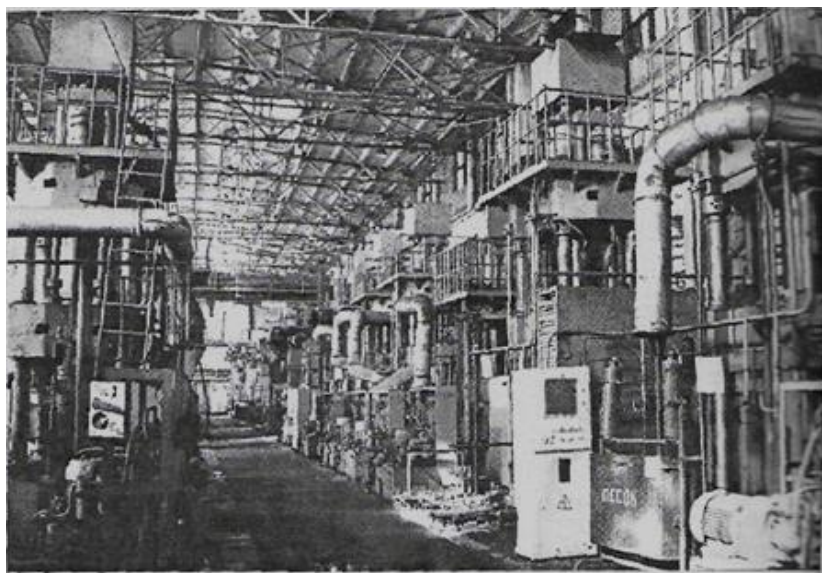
Участок гидравлических прессов для изотермической штамповки лопаток компрессора.
